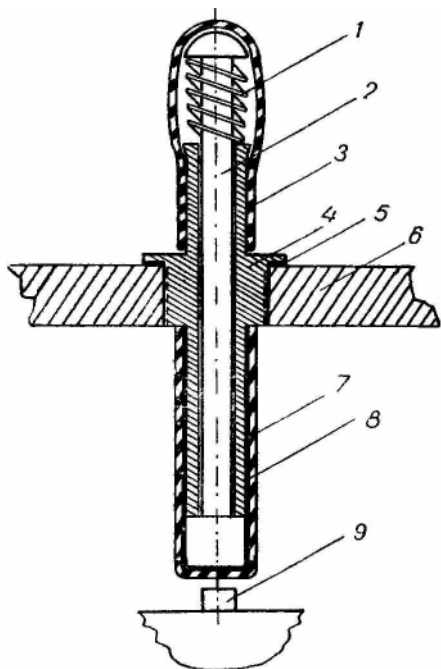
Герметизирующее устройство: 1 — пружина возврата кнопки; 2 — стержень; 3 — резиновая оболочка (от пипетки); 4 — корпус герметизирующего устройства; 5 — уплотнительная прокладка; 6 — стенка бокса; 7 — резиновая оболочка (от пипетки); 8 — трубка из латунной фольги, плотно насаженная на корпус (служит для предотвращения попадания резины между корпусом и стержнем в момент нажатия кнопки); 9 — кнопка спуска затвора аппарата
